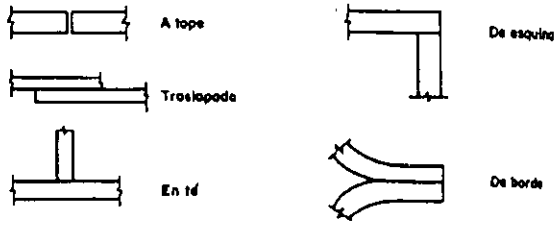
Distintos tipos de soldadura utilizados para cada junta
